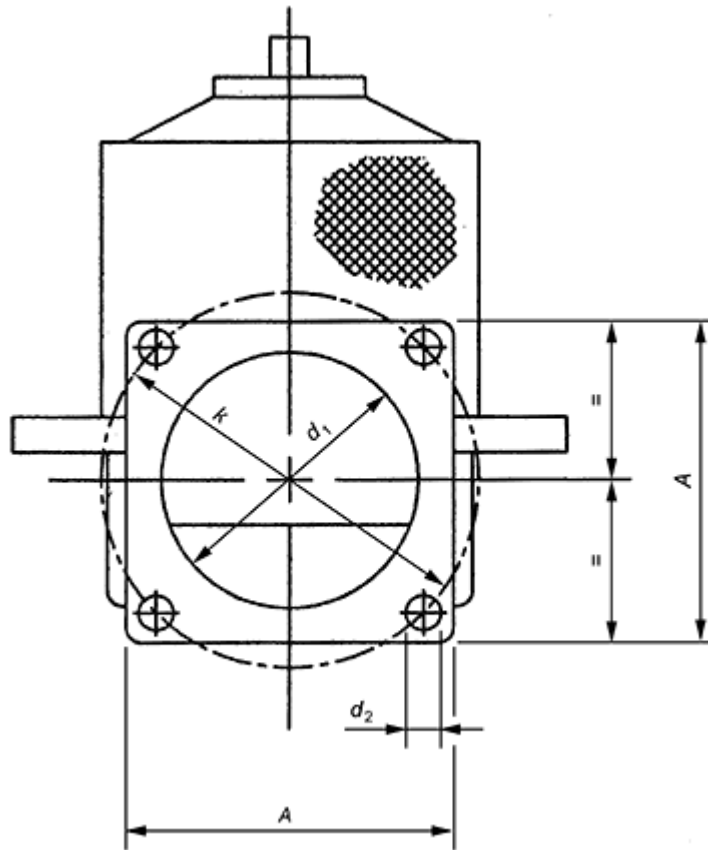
Присоединительные размеры сливного фланца для приемного клапана (квадрат)
